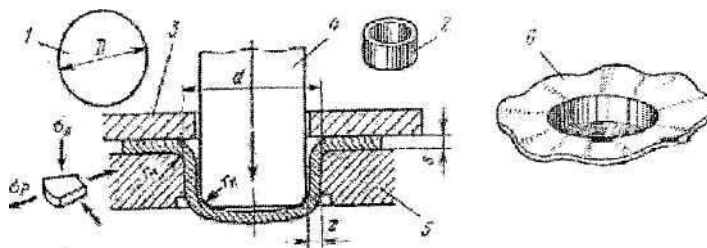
Схема вытяжки: 1 - заготовка; 2 - изделие; 3 - прижим; 4 - пуансон; 5 - матрица; 6 - изделие со складками, образующимися при вытяжке без прижима
